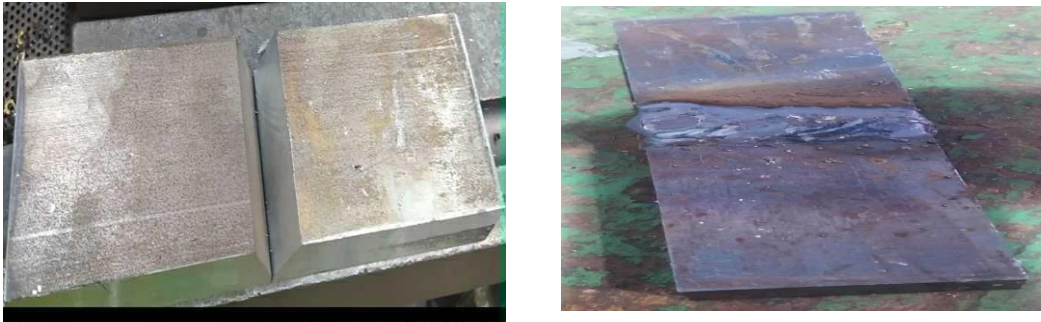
Forme de l'échantillon avant et après le soudage
